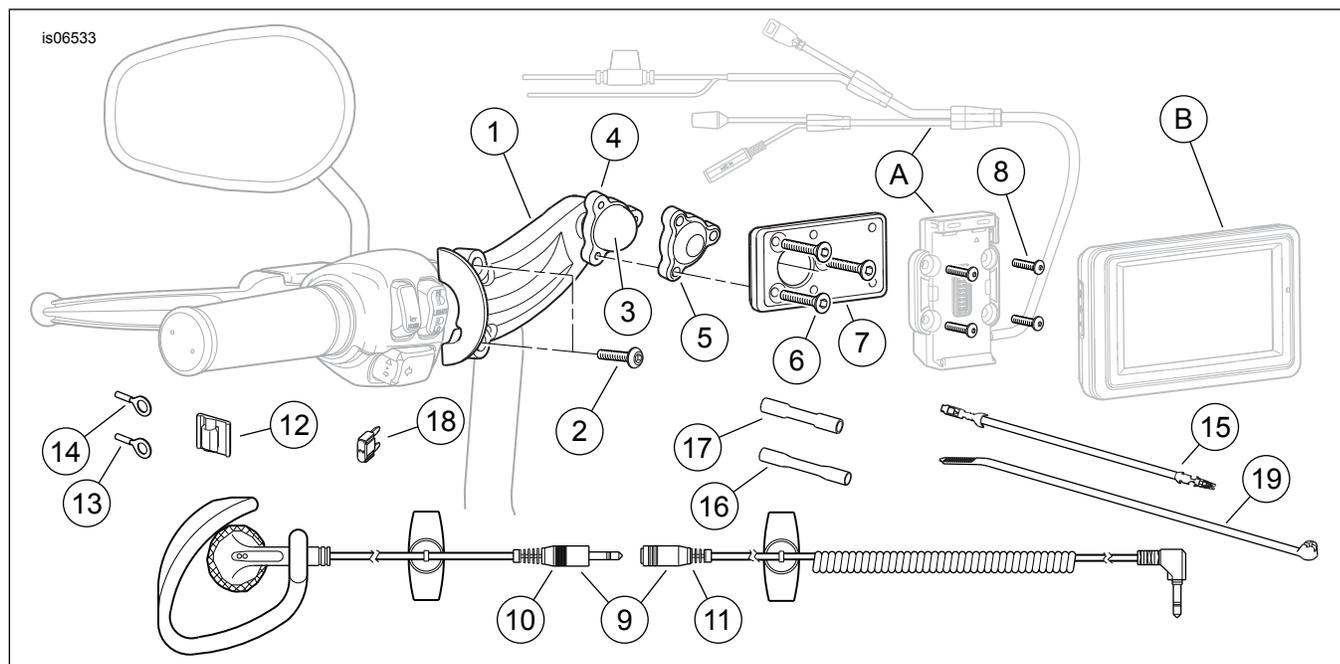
Pièces de rechange, kit de montage sur guidon de GPS Road Tech Zumo 660 et Zumo 665
